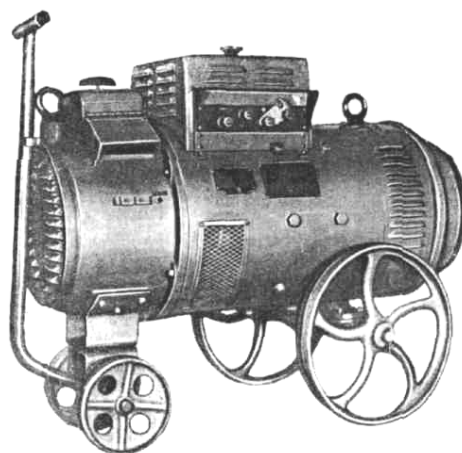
Сварочный преобразователь ПСО-500
